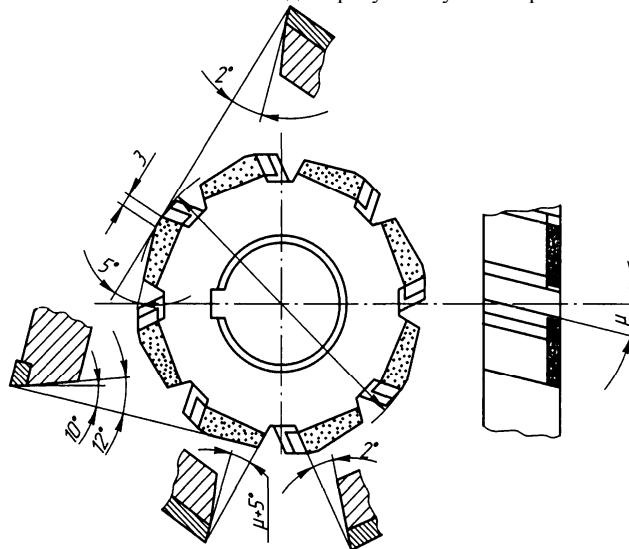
Инструмент в виде плоского диска с напайными твердосплавными пластинами
